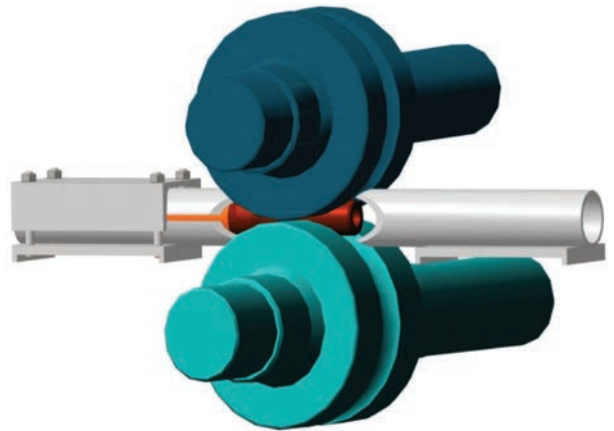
Зовнішній вигляд розміщення валків з провідками вою прокаткою, проведено тестові випробування на модельному матеріалі — алюмінії. Заготовка виготовлялася за кресленнями композиційного перехідника.
